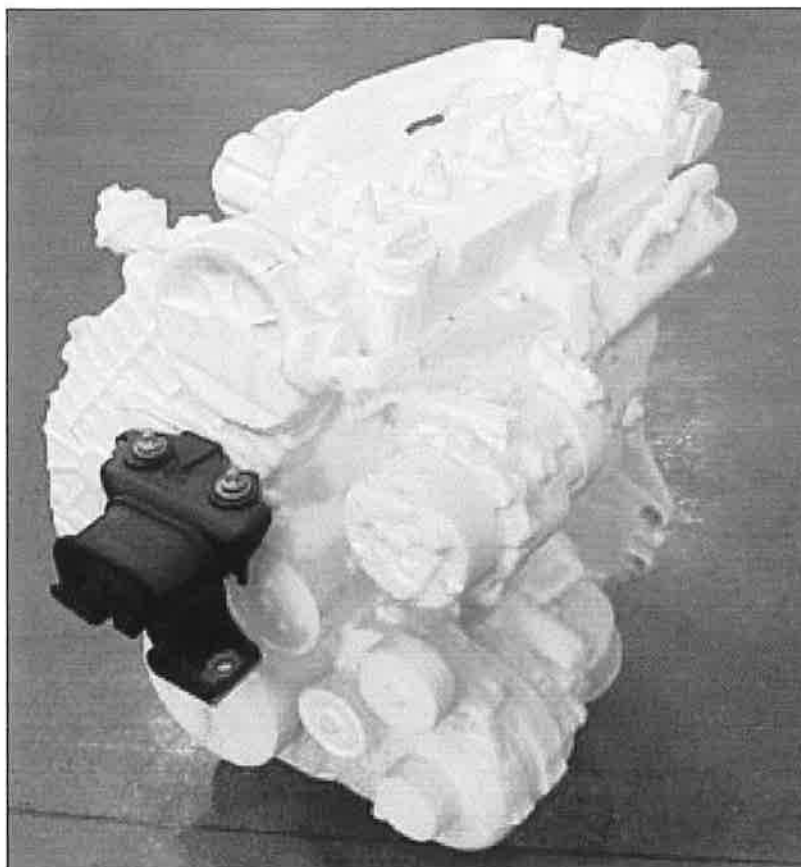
Modelo usinado de um motor completo com um suporte montado. (Macarrão, 2004).
